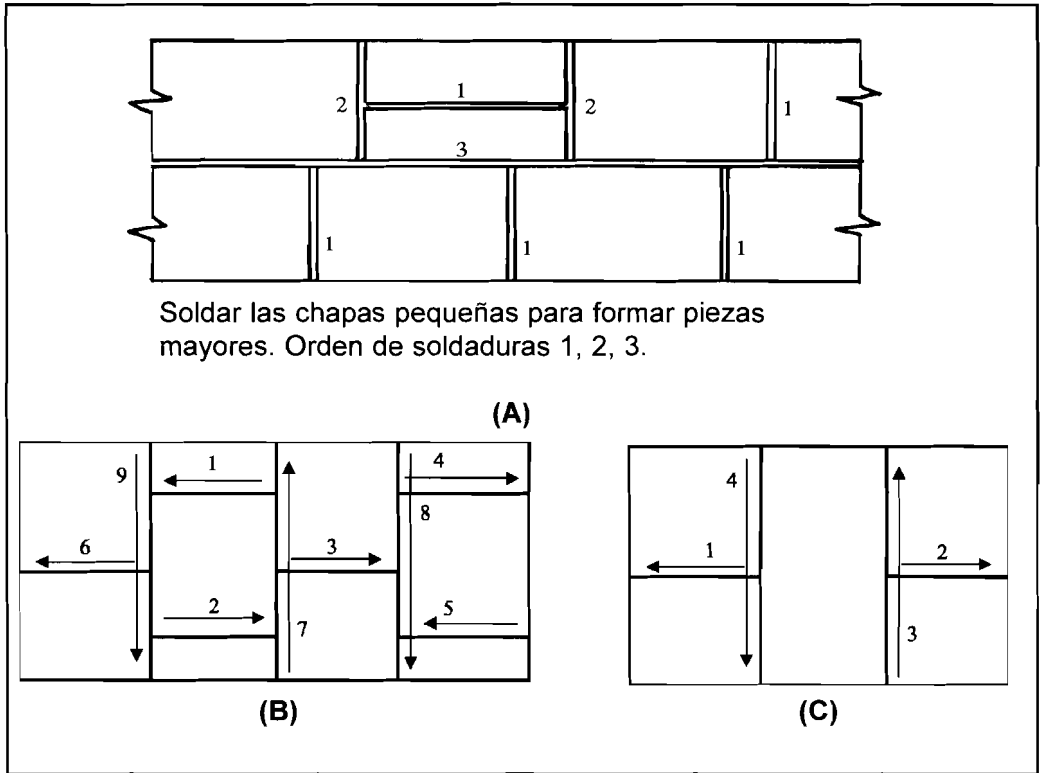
SOLDEO DE UN CONJUNTO DE CHAPAS
